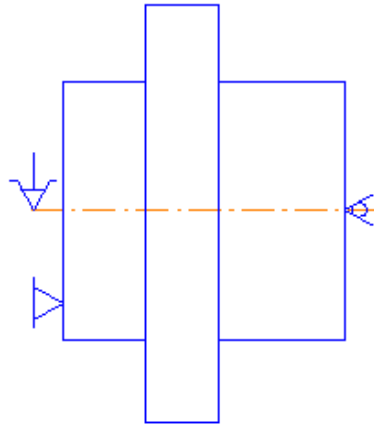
Типова схема базування маточини в процесі виготовлення
